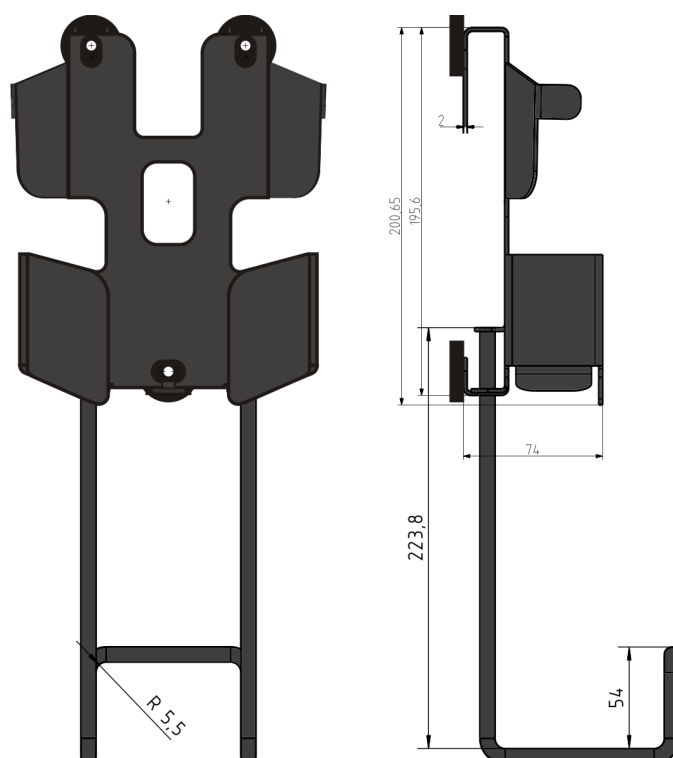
Rück- und Seitenansicht der Wandhalterung KeTop WB025 / WB026, (Maßangaben in mm)
